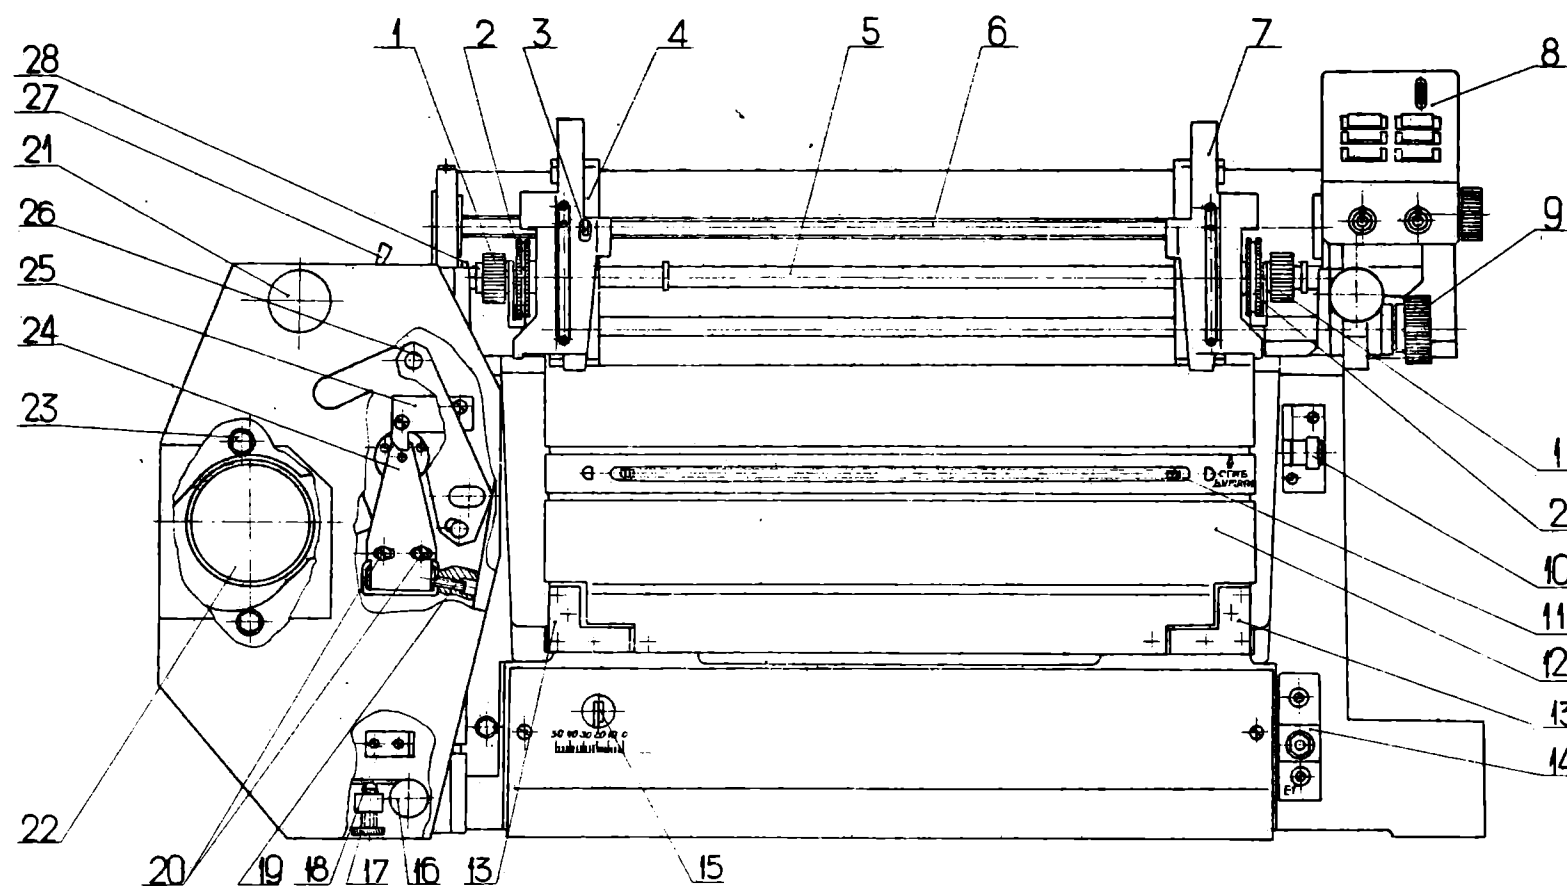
Механизм печатающий. Механизм барабана открыт. Главный вид.
